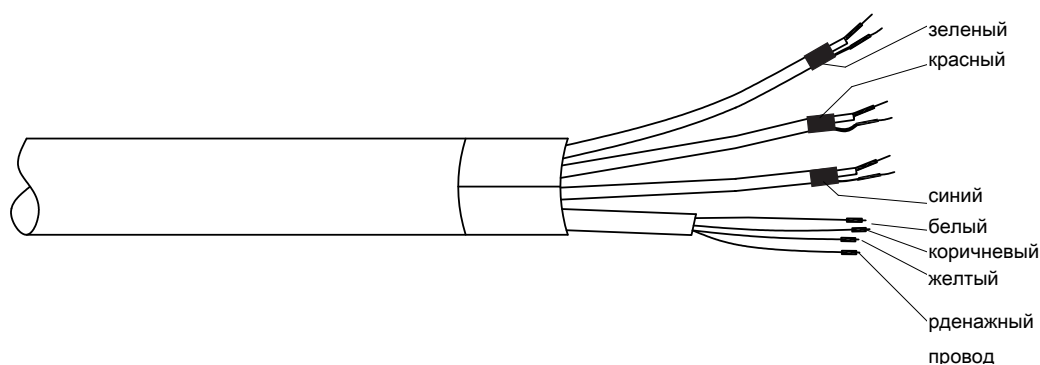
Стандартный соединительный кабель с концевой заделкой L₀₀₀, сторона измерительного преобразователя
